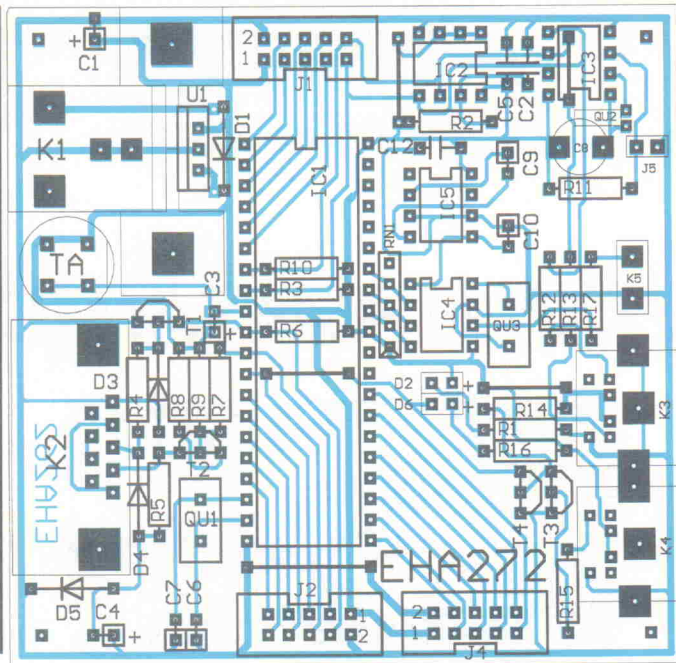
Setzt man beim Prototyper für IC2 einen 24C16 ein, darf die I²C-Uhr IC3 nicht gleichzeitig bestückt sein.
